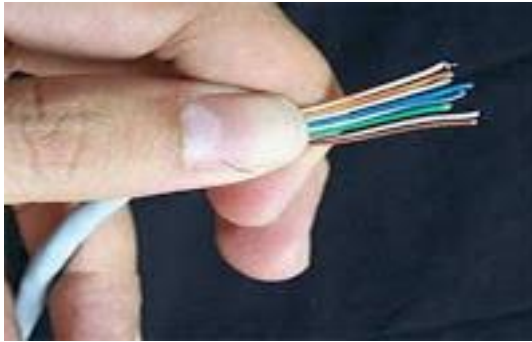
Hasil Pengupasan Kabel Menggunakan Tang Crimping
